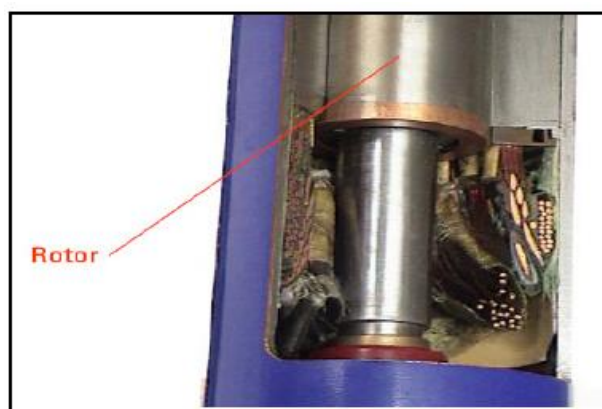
Segmento en corte del rotor<sup>6</sup>.
